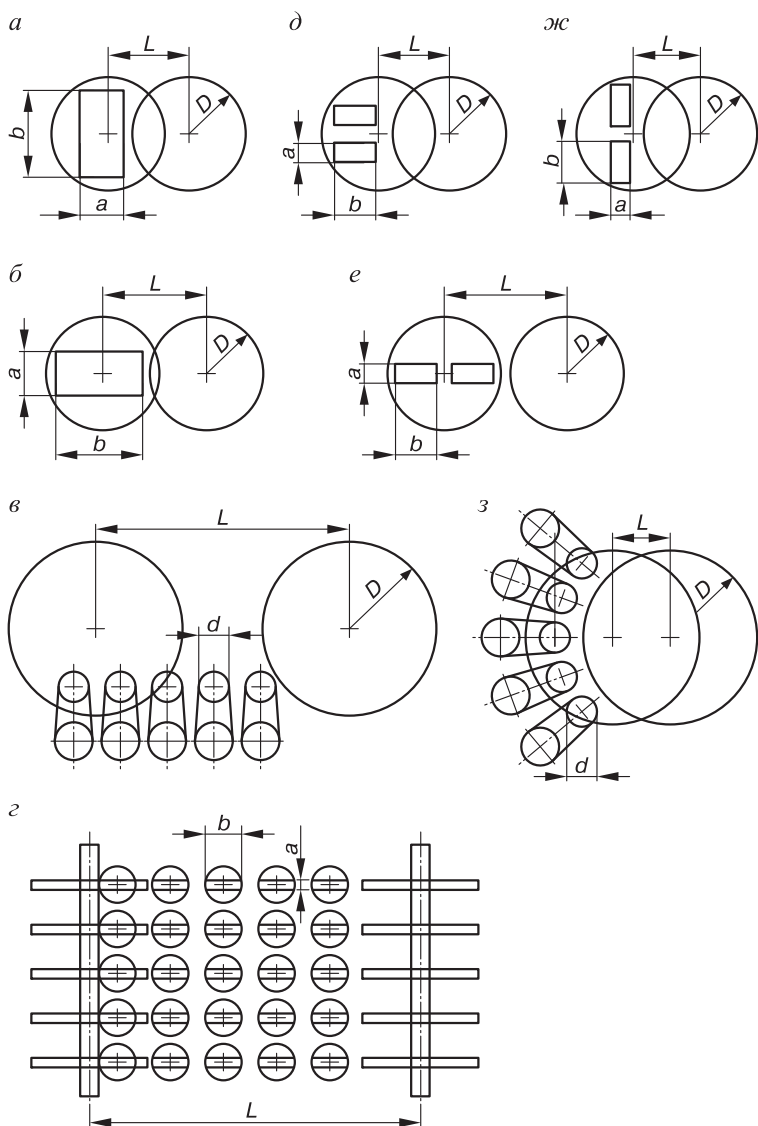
Схемы установок заготовок по отношению к фрезам:
